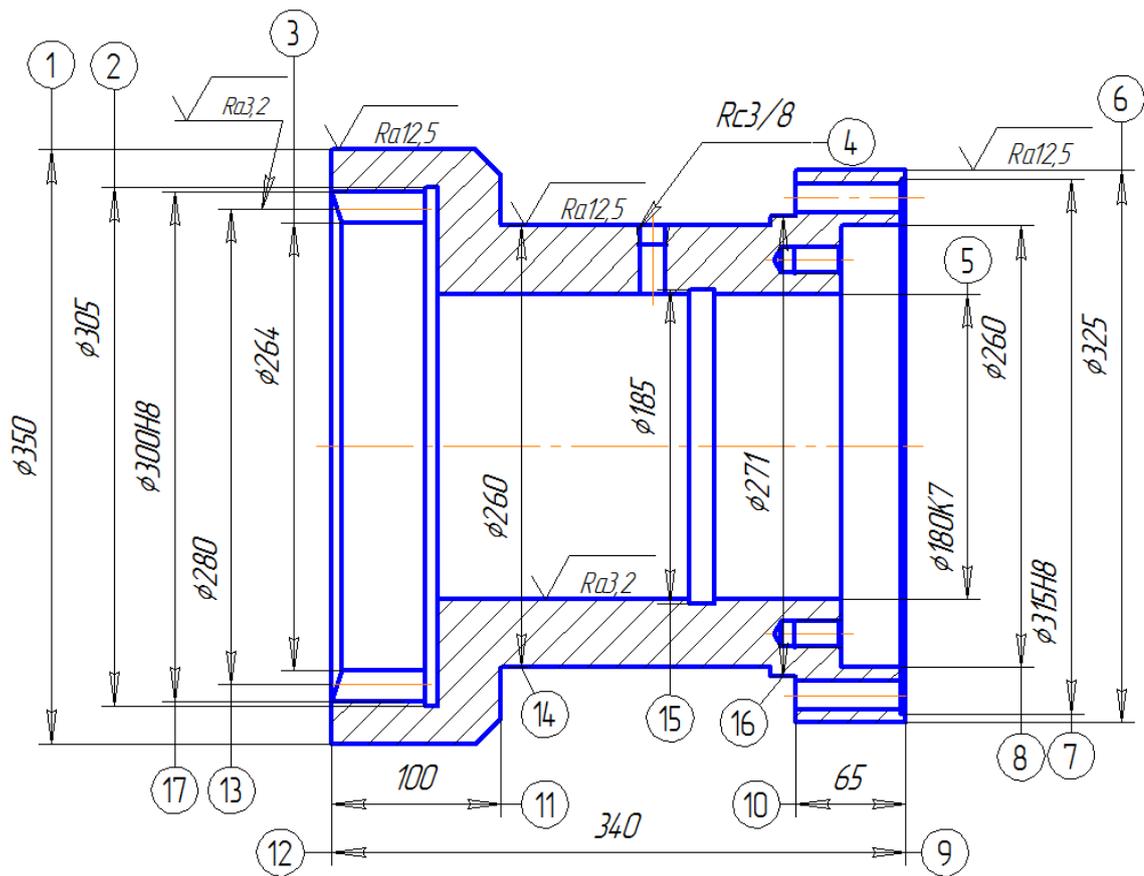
Эскиз детали «Ступица для запасного привода буровой установки»
